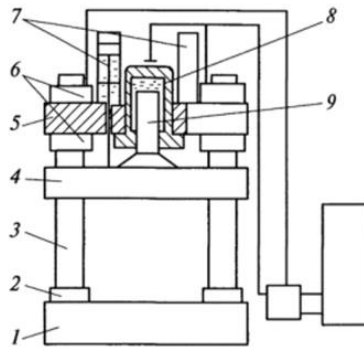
Схема гідравлічного преса: 1 — основа; 2, 6 — гайки; 3 — направляючі колони; 4— рухома плита; 5 — архітрав (нерухома плита); 7— зворотні циліндри; 9 — плунжер
